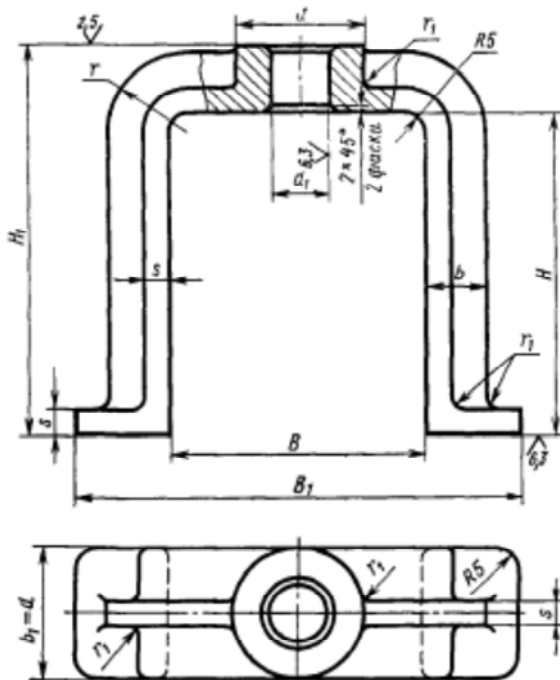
Скоба винтового приспособления для удаления стержней
